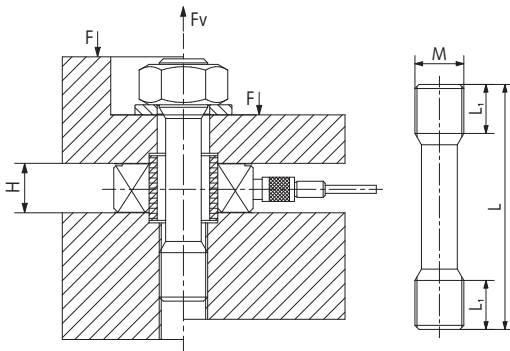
Einbau mit Vorspannsatz Typ 9420A...
